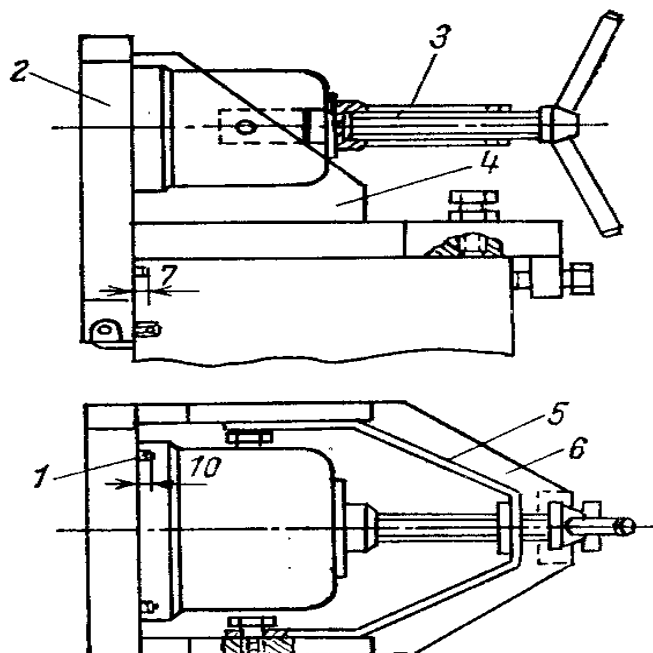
Пристосування для розточування корпусу насоса на токарному верстаті:
